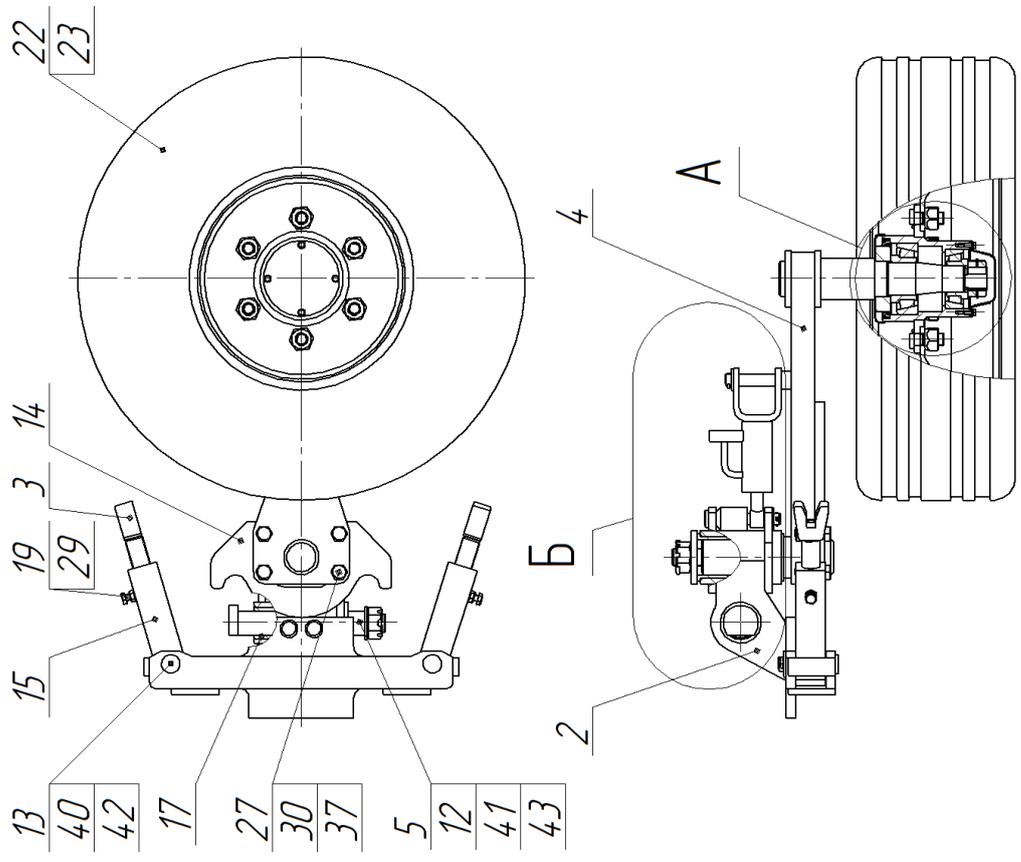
ПОМ-8 15.00.000 Колесо
